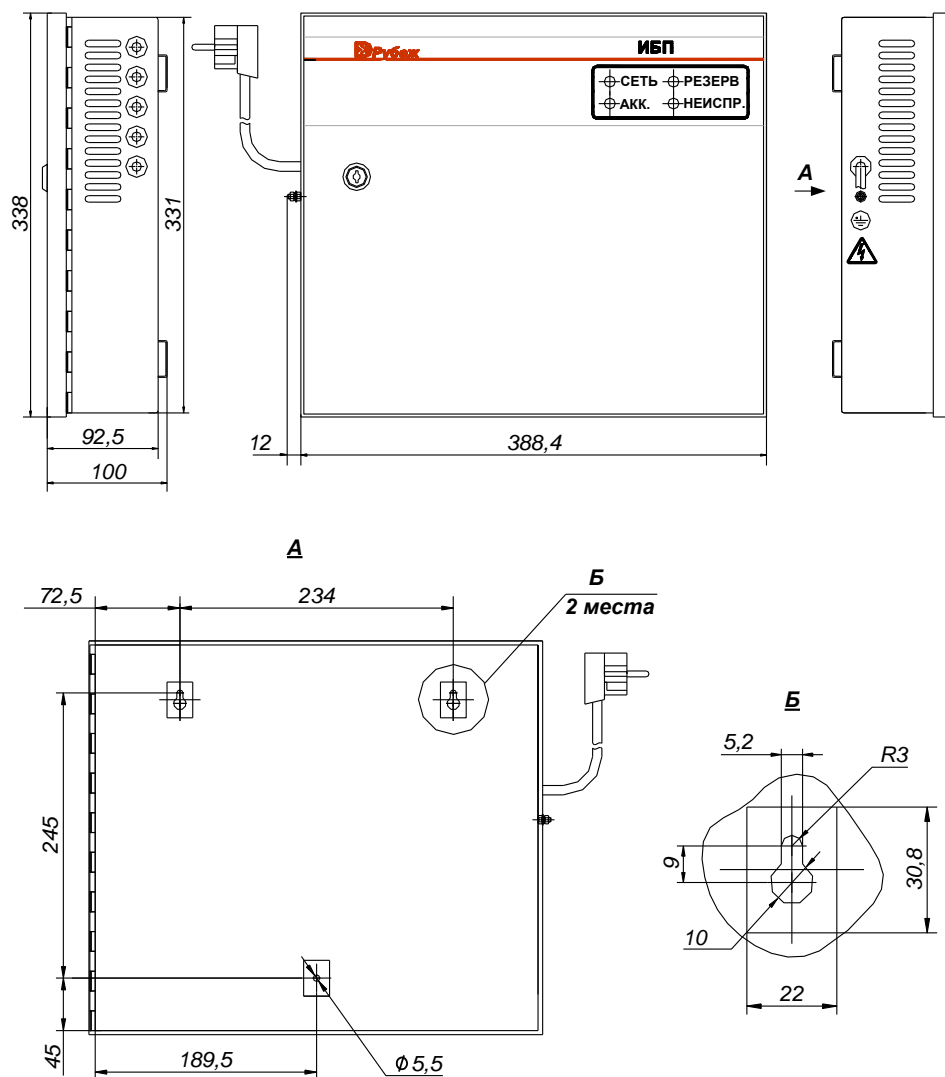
Присоединительные размеры ИБП 1200/2400 исп. 1
